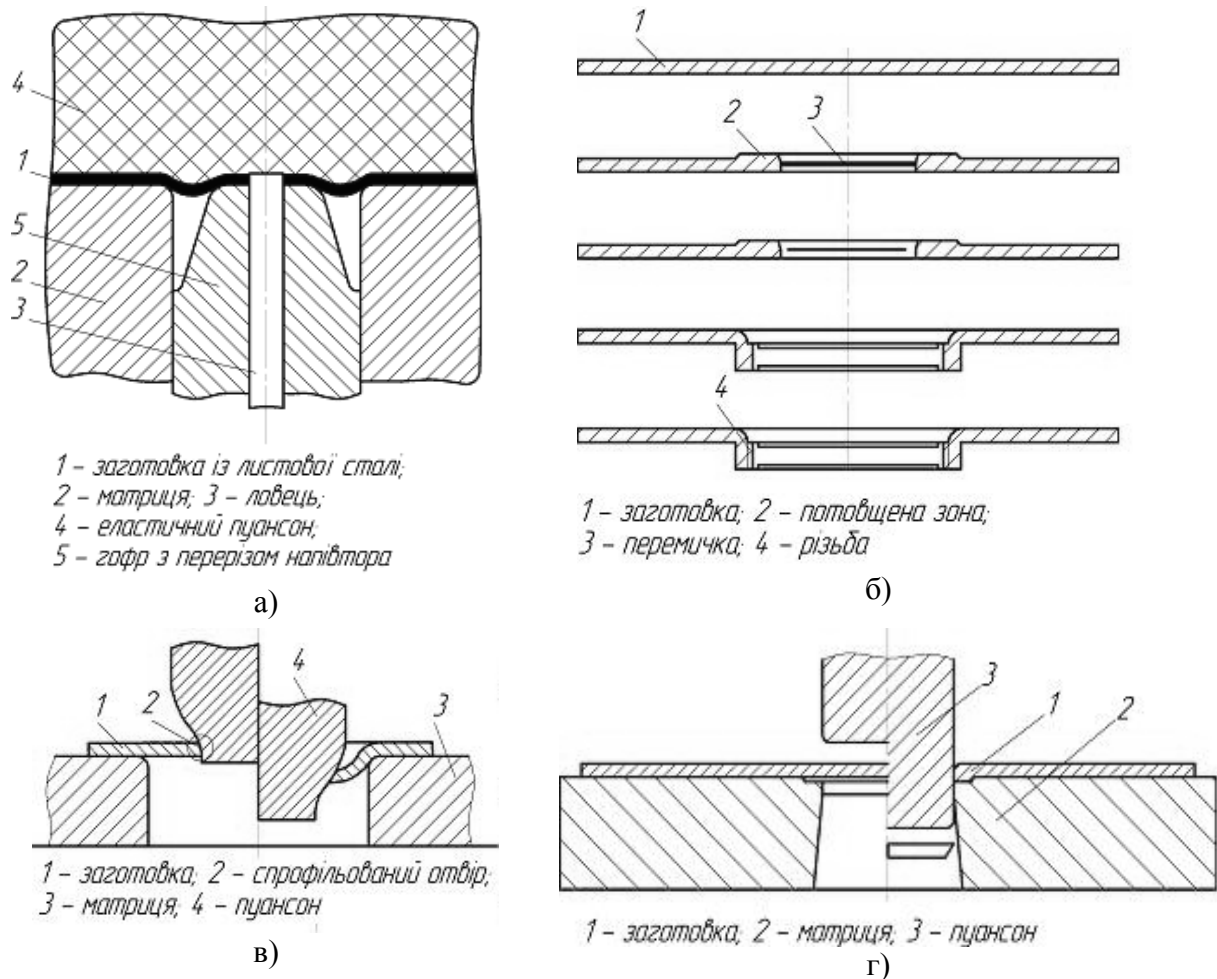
Існуючі способи відбортування для зменшенні різностінності відбортованої частини заготовки
